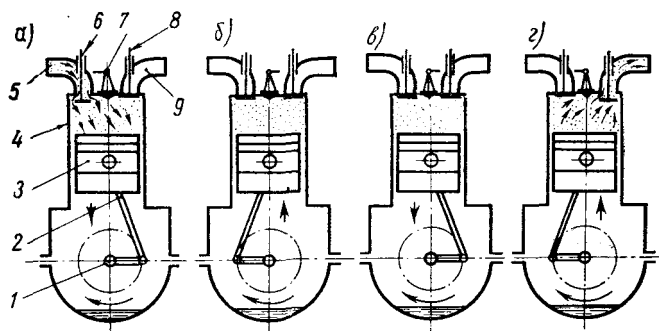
Рабочий процесс четырехтактного карбюраторного двигателя
